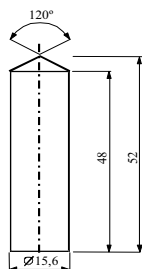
Êmbolo cilíndrico de bronze, dimensões em mm
